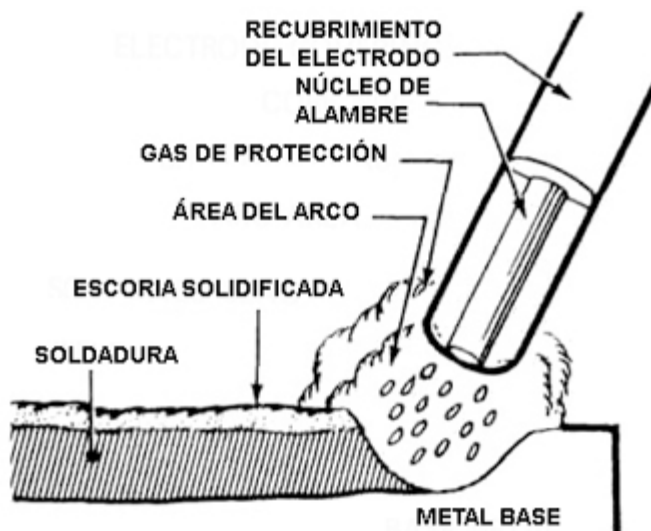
Soldadura de arco (sapiensman.com).
